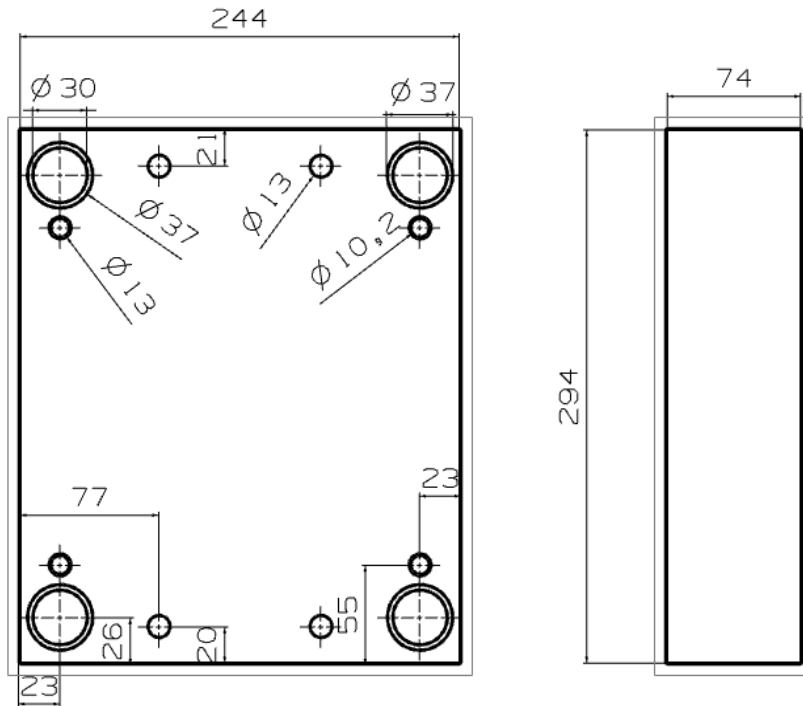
Dimensiones placa posterior de cavidad P2
